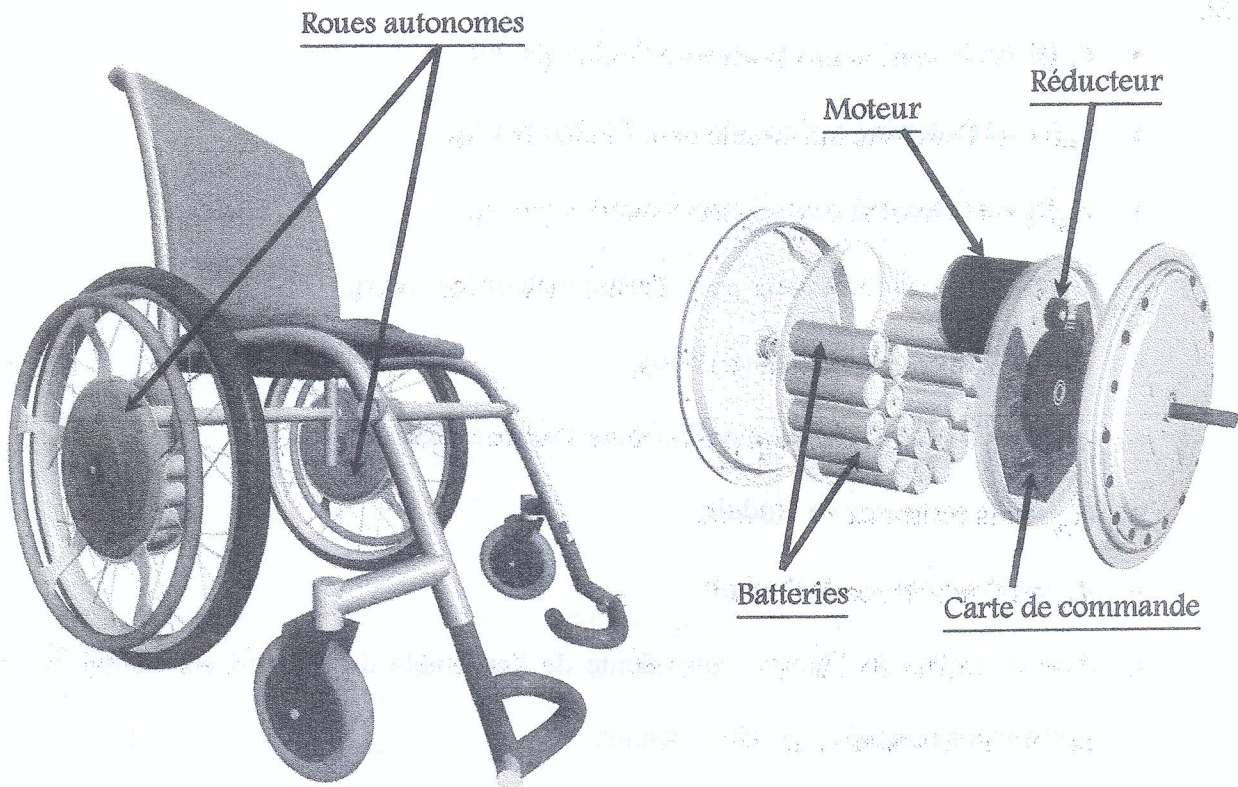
Prototypage de fauteuil roulant équipé de deux roues autonomes
